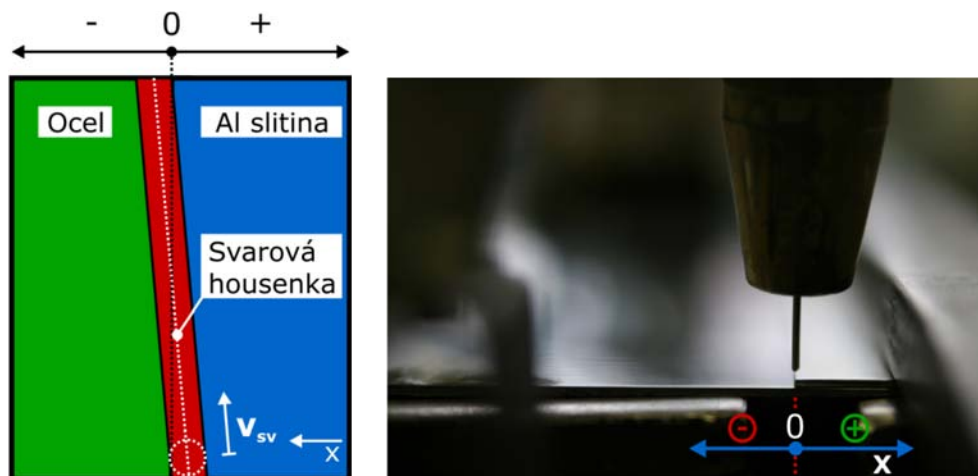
Schematické znázornění uspořádání plechů pro spojení
